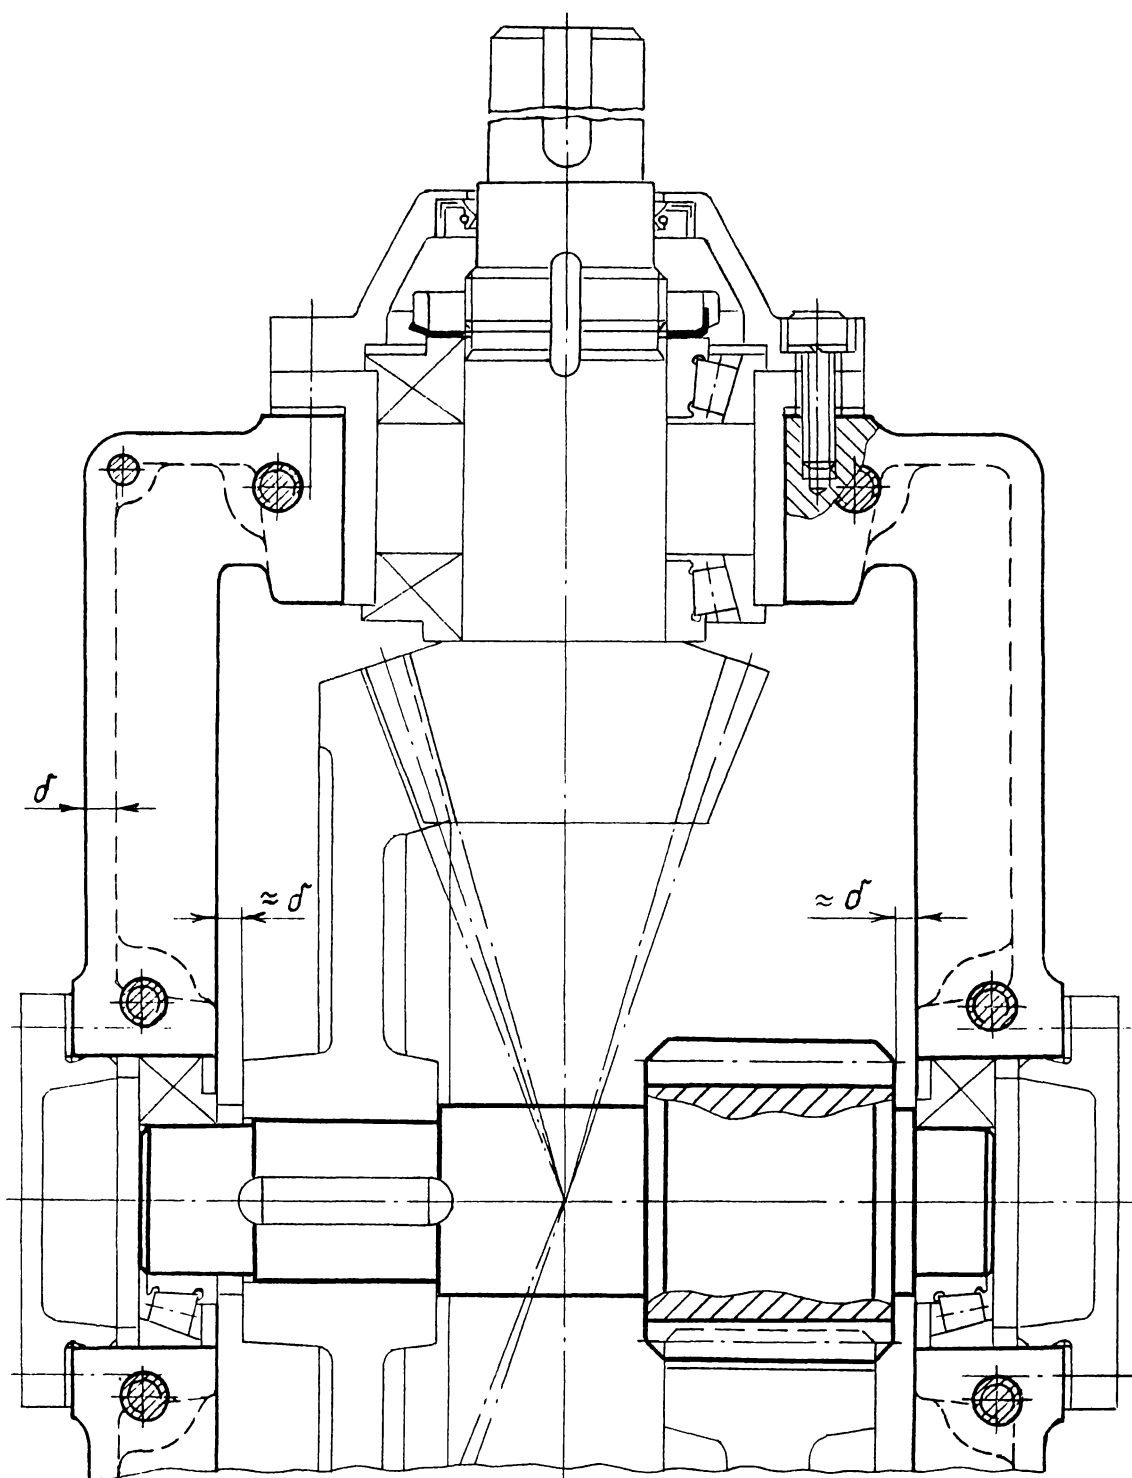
Промежуточный вал коническо-цилиндрического двухступенчатого горизонтального редуктора
